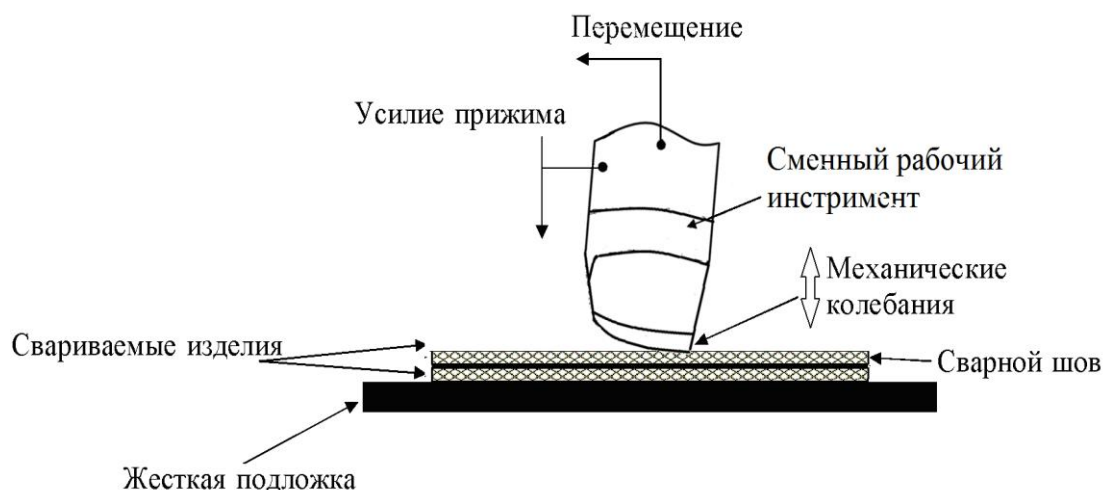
Схема ультразвуковой сварки с одновременной обрезкой
